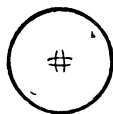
Разметка центра заготовки с помощью разметочного циркуля.
